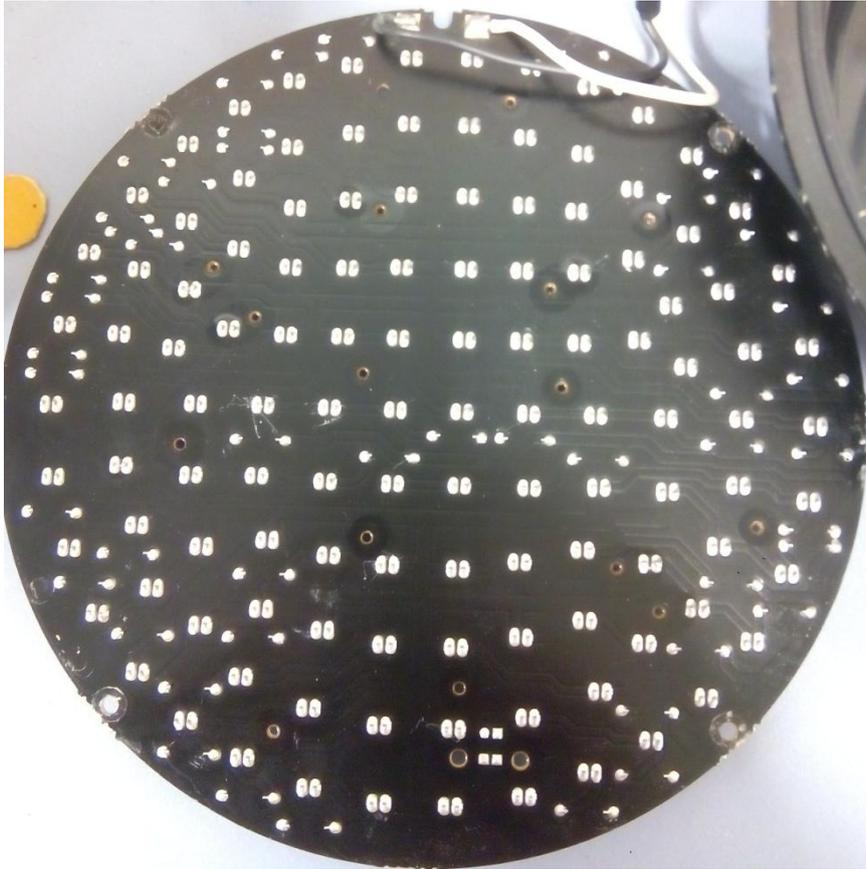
Placa PCB disco led con soldadura fria.
